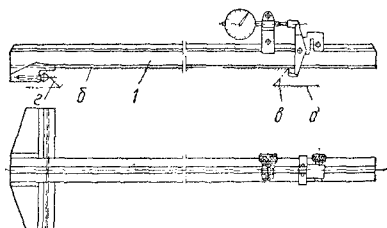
Подставка для крепления индикаторной головки с базированием на внутренние призматические направляющие.
